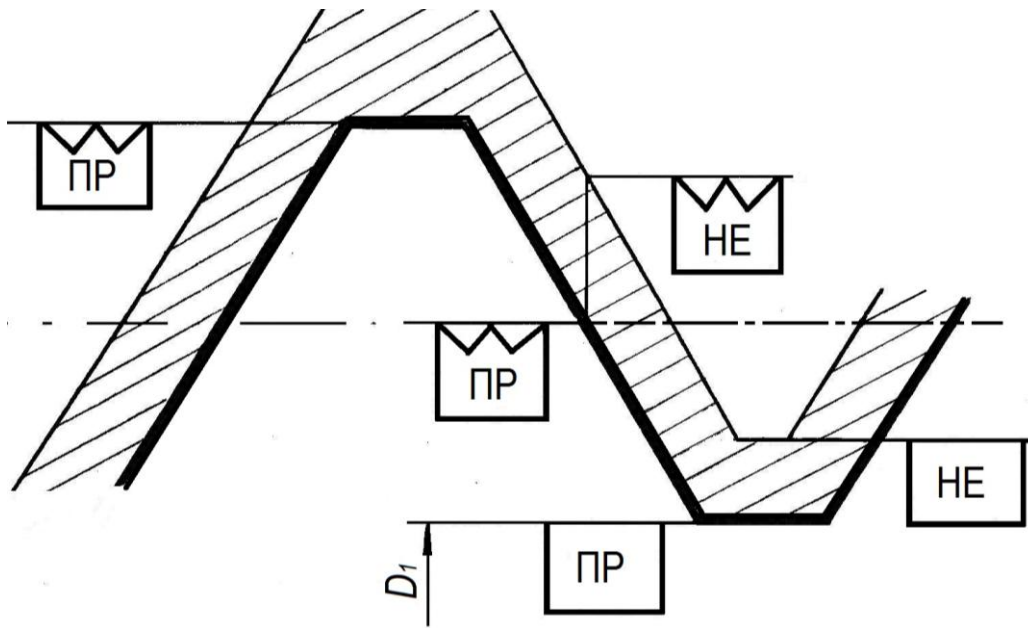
Схема контроля предельными калибрами наружной резьбы
